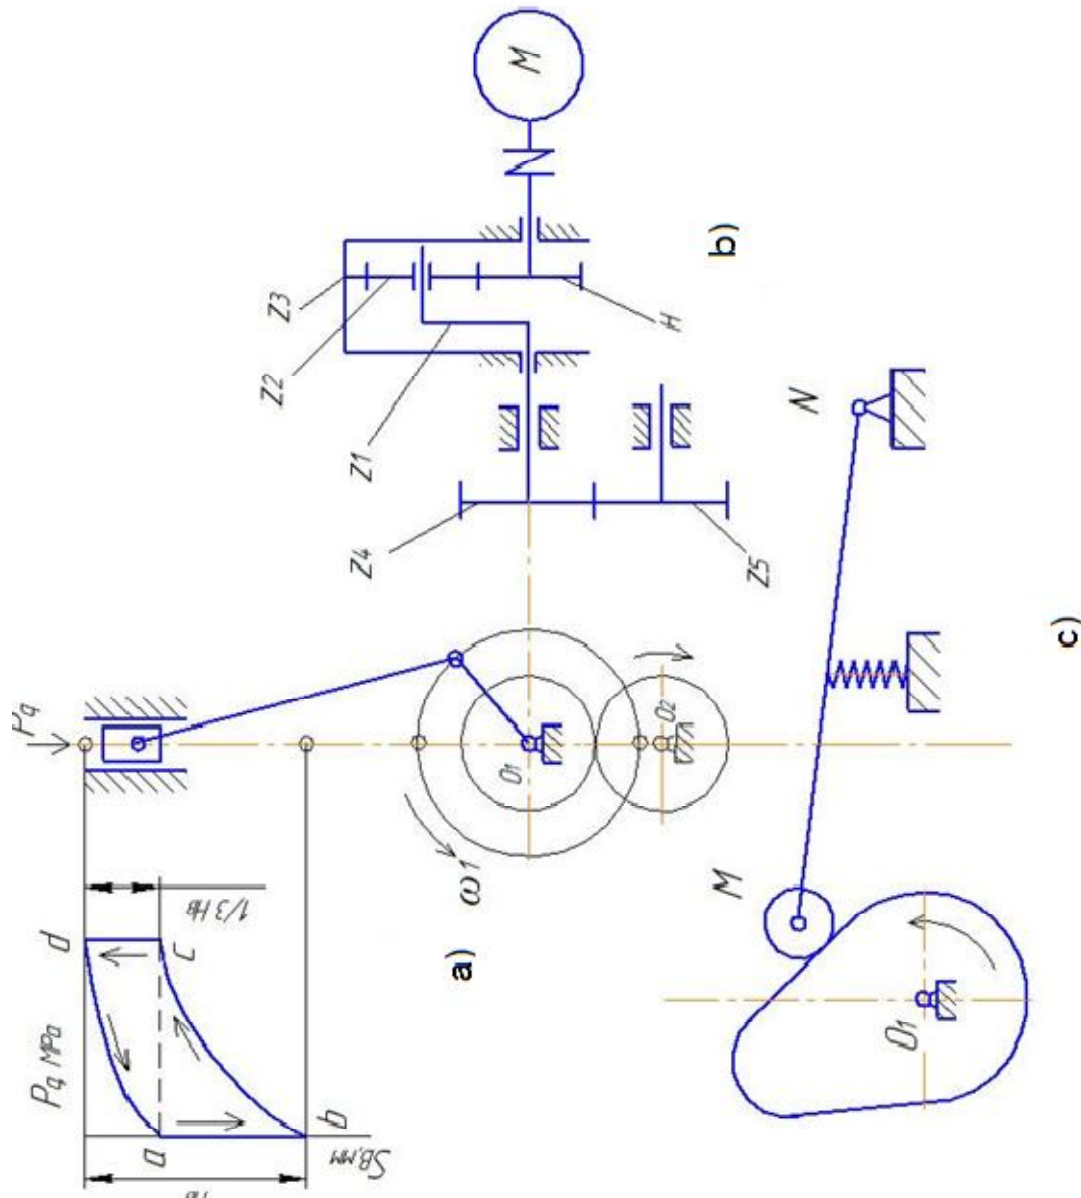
Кинематическая схема одноступенчатого поршневого компрессора
